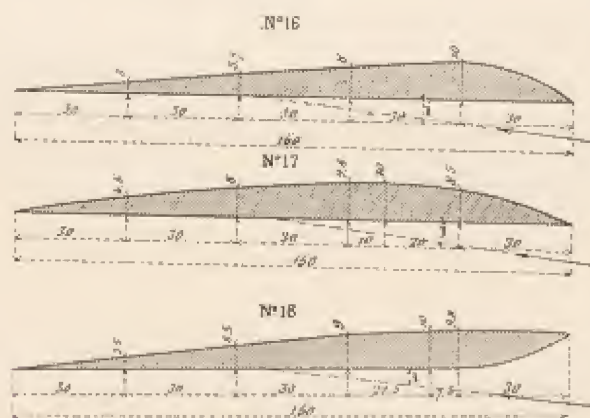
Profils des ailes n° 16, 17 et 18.
